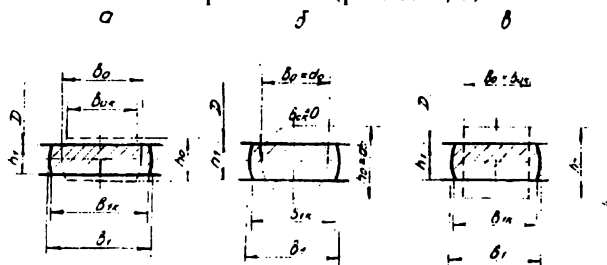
Схемы для расчета вытяжки при прокатке в гладких валах полосовой (а), круглой (б) и квадратной (в) заготовок
